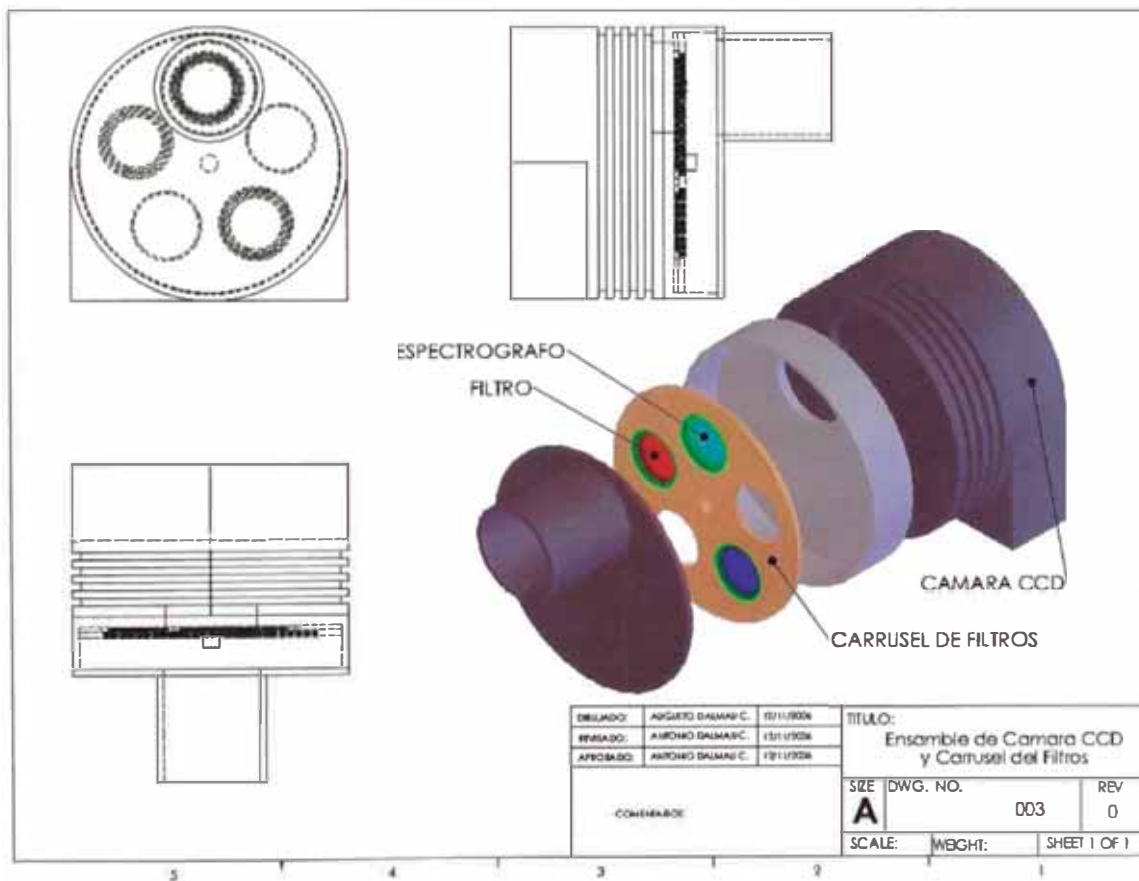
Montaje del carrusel del filtros con la cámara CCD
